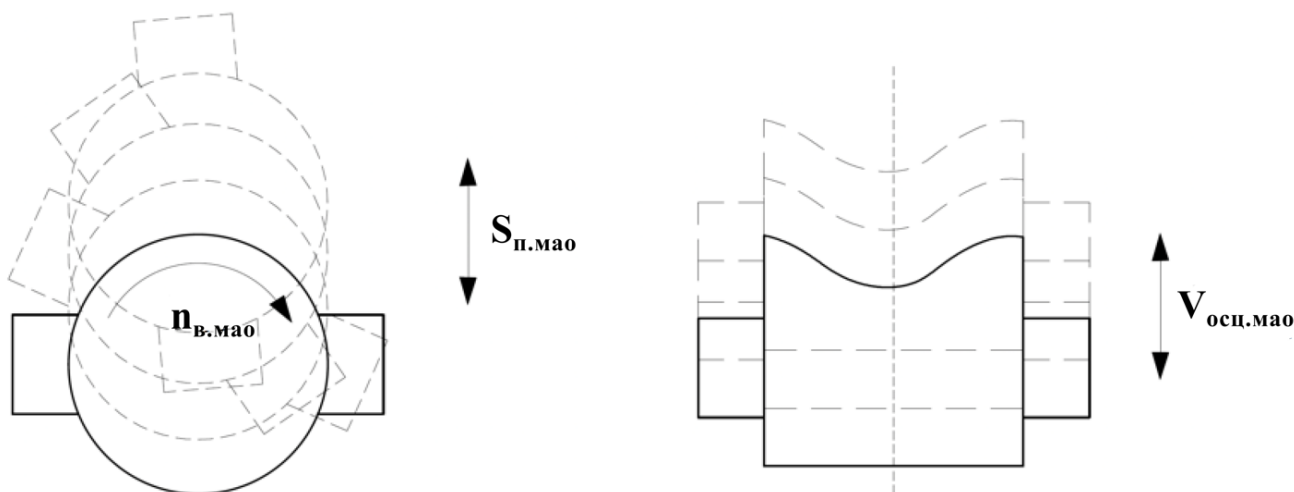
Движение заготовки при магнитно-абразивной обработке
